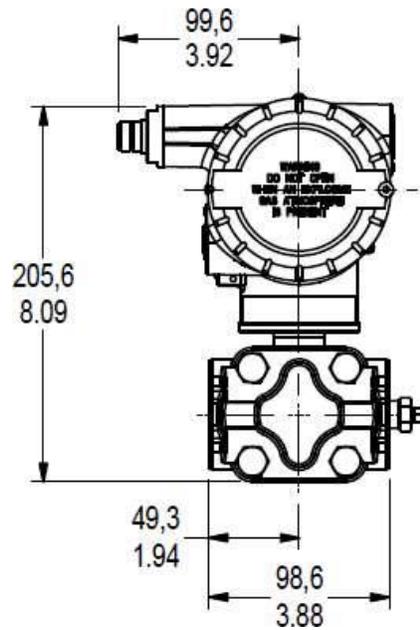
Jauge à deux têtes, dimensions de montage typiques pour STGW740, STGW770 (adaptateur d'antenne à distance montré, vue arrière)
